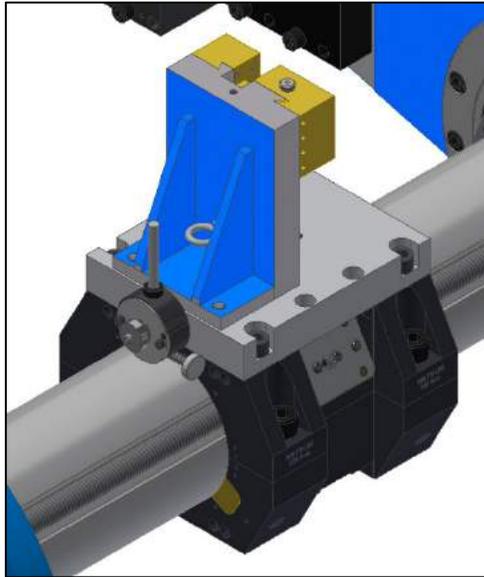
Planfräskopf direkt am Werkzeugträger montiert
